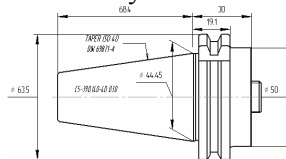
Базовый держатель C5-390.140-40 030
